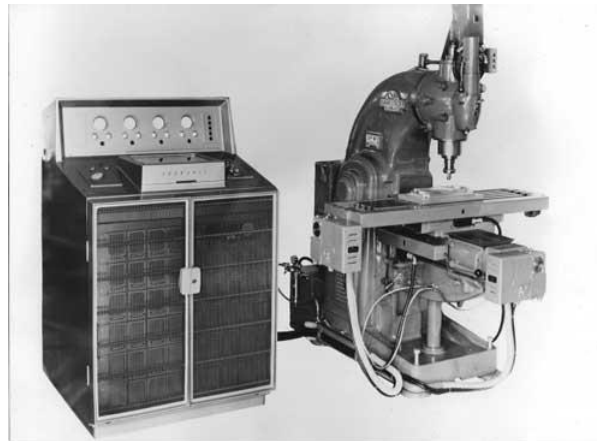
Primera máquina herramienta CNC fabricada en Europa [6].
